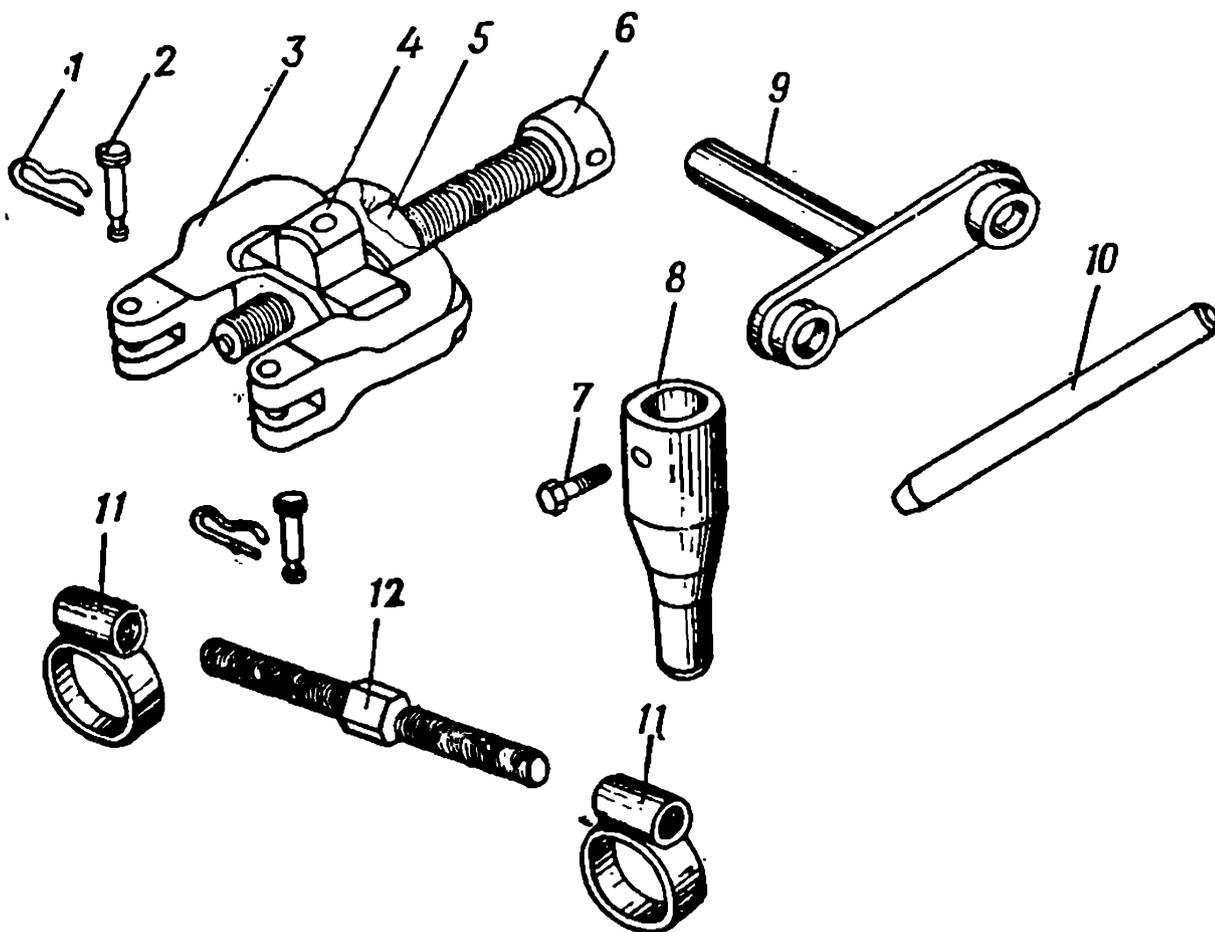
Комплект приспособлений для замены пальцев гусеницы с закрытым шарниром:
